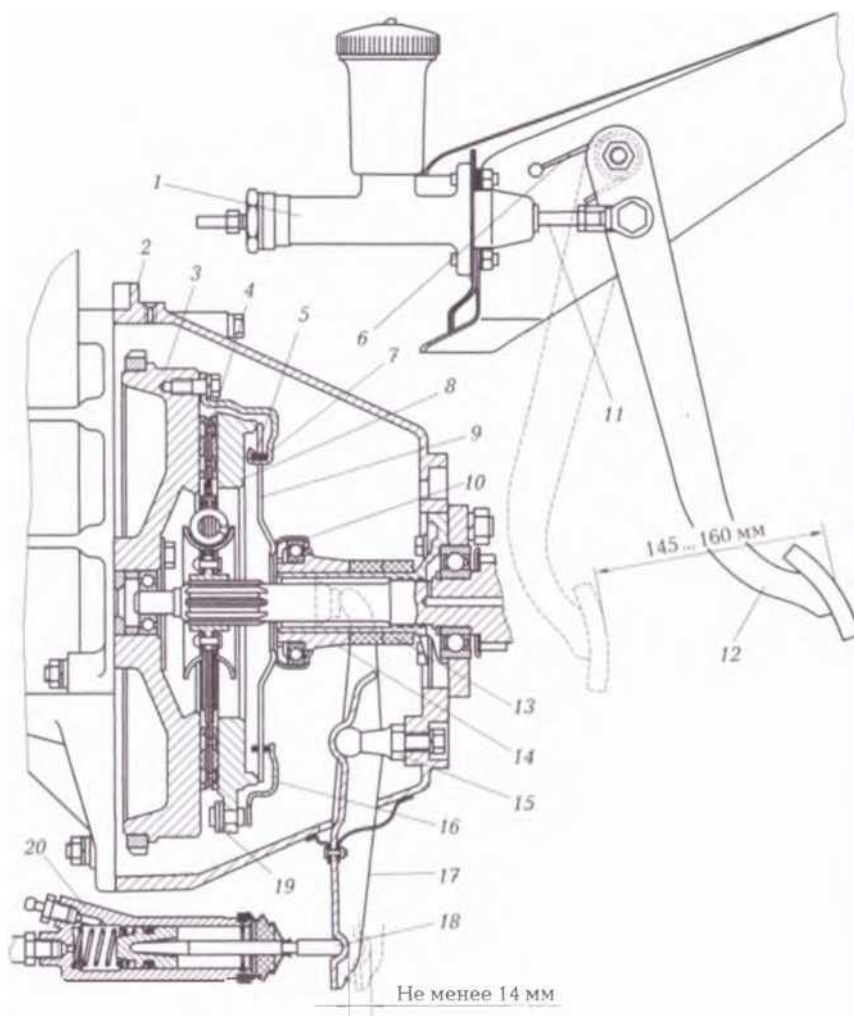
Сцепление диафрагменного типа и привод выключения сцепления:
